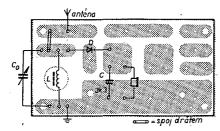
Obrazec plošných spojů destičky Smaragd E50
